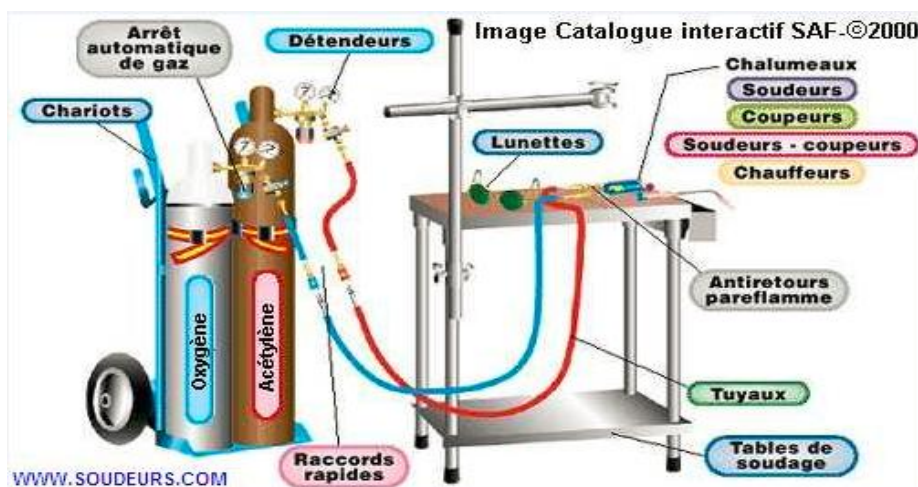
Croquis didactique du procédé de soudage oxyacétylénique [16]
